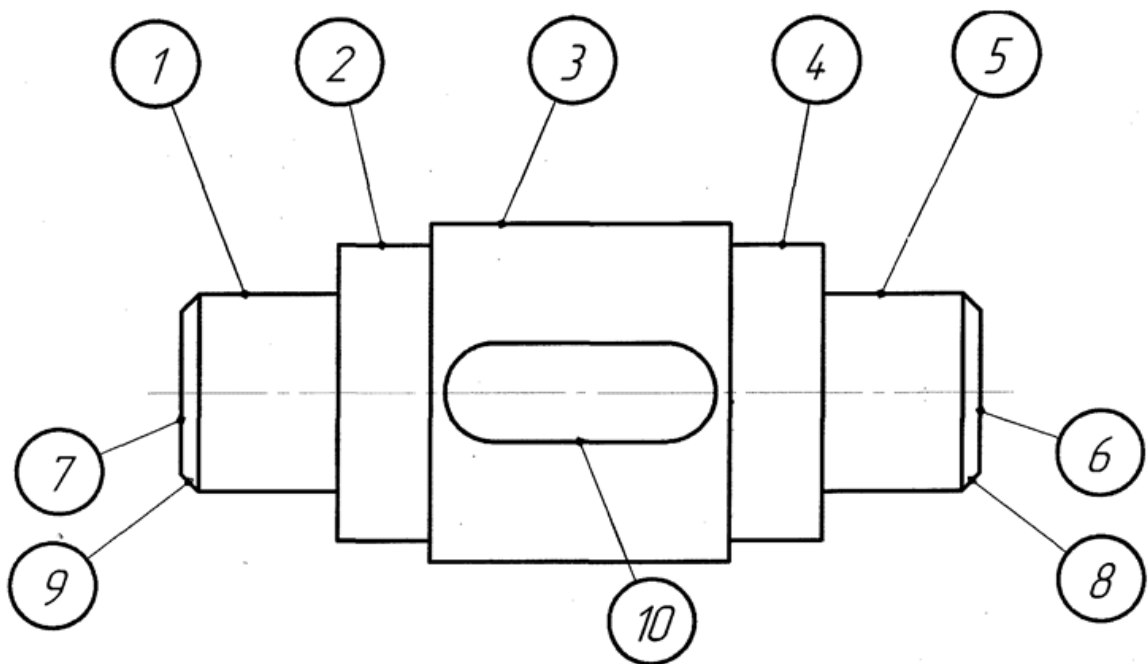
Ескіз деталі з проставленими поверхнями.
